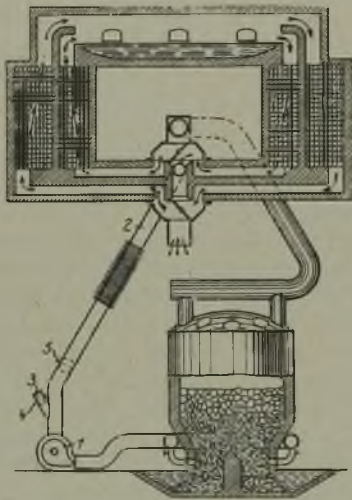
Gaserzeuger der Eldred Process Co. für einen Schmelzofen mit Regenerativfeuerung.
